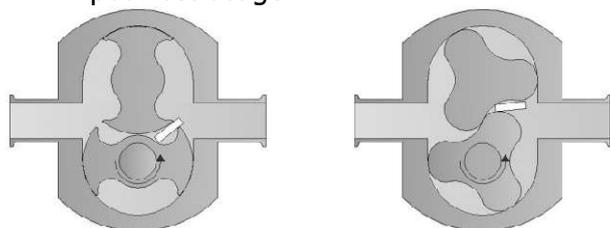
Desserrer le boulon du rotor (rotor inférieur)
